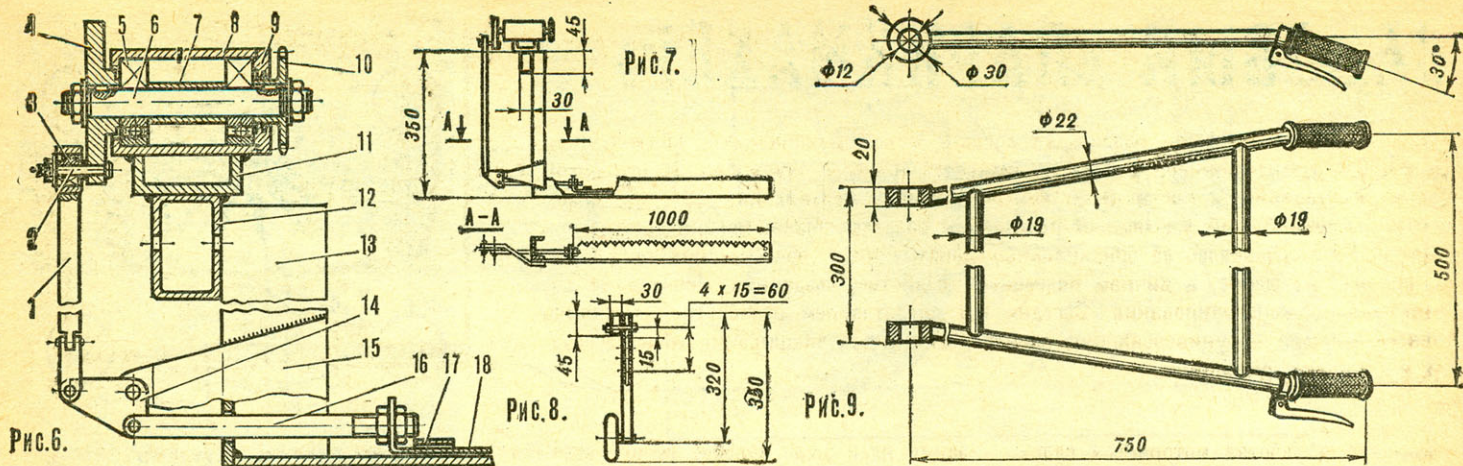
Вал отбора мощности с приводом косилки: 1 — шатун, 2 — палец, 3 — сферический подшипник, 4 — кривошипное колесо, 5 — подшипник № 60302, 6 — вал, 7 — распорная втулка, 8 — корпус, 9 — крышка с фетровым сальником, 10 — звездочка, 11 — проставка, 12 — кронштейн корпуса, труба 45×30×2,5 мм, 13 — стойка, 14 — качалка, 15 — кронштейн, 16 — шток подвижного ножа, 17 — направляющая, 18 — подвижный нож косилки.
